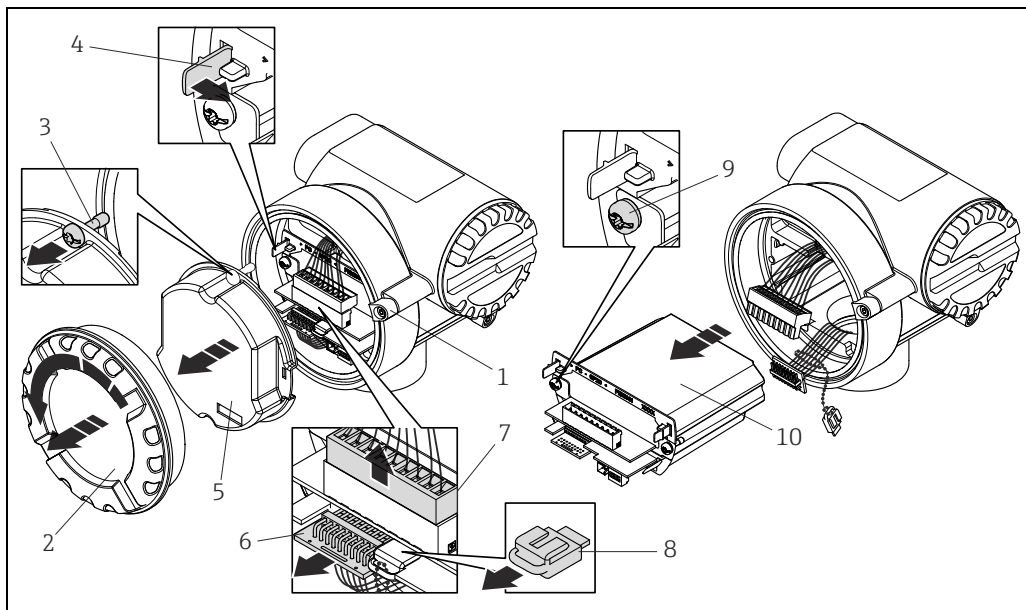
Remoção e instalação de componentes eletrônicos do medidor
